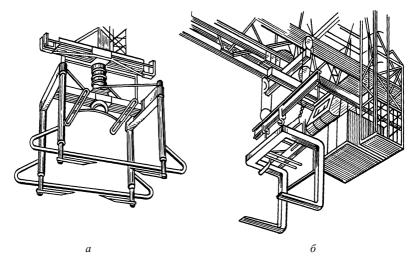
Крановые захваты для пакетов пиломатериалов: a – портального типа; δ – вилочного типа
